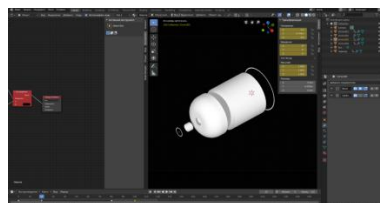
Демонстрация видов сварных соединений для изготовления сварной конструкции «Разъемный сосуд»
